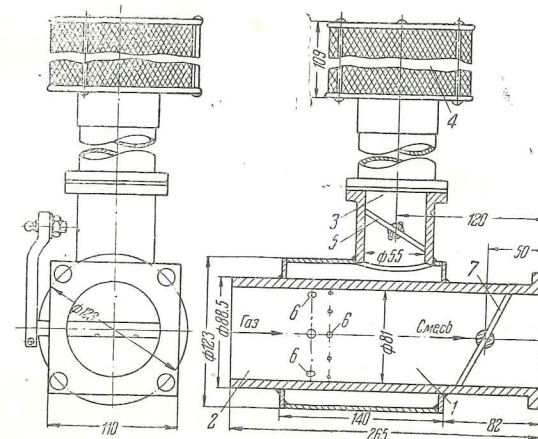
Схема смесителя установки „Гумбольдт-Дейтц“
